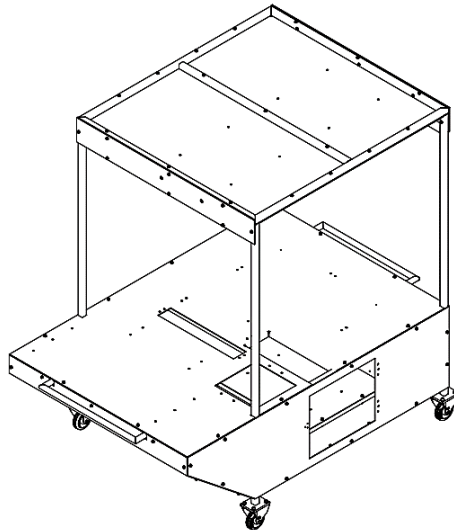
Vista isométrica del plano de ensamble de la estructura
